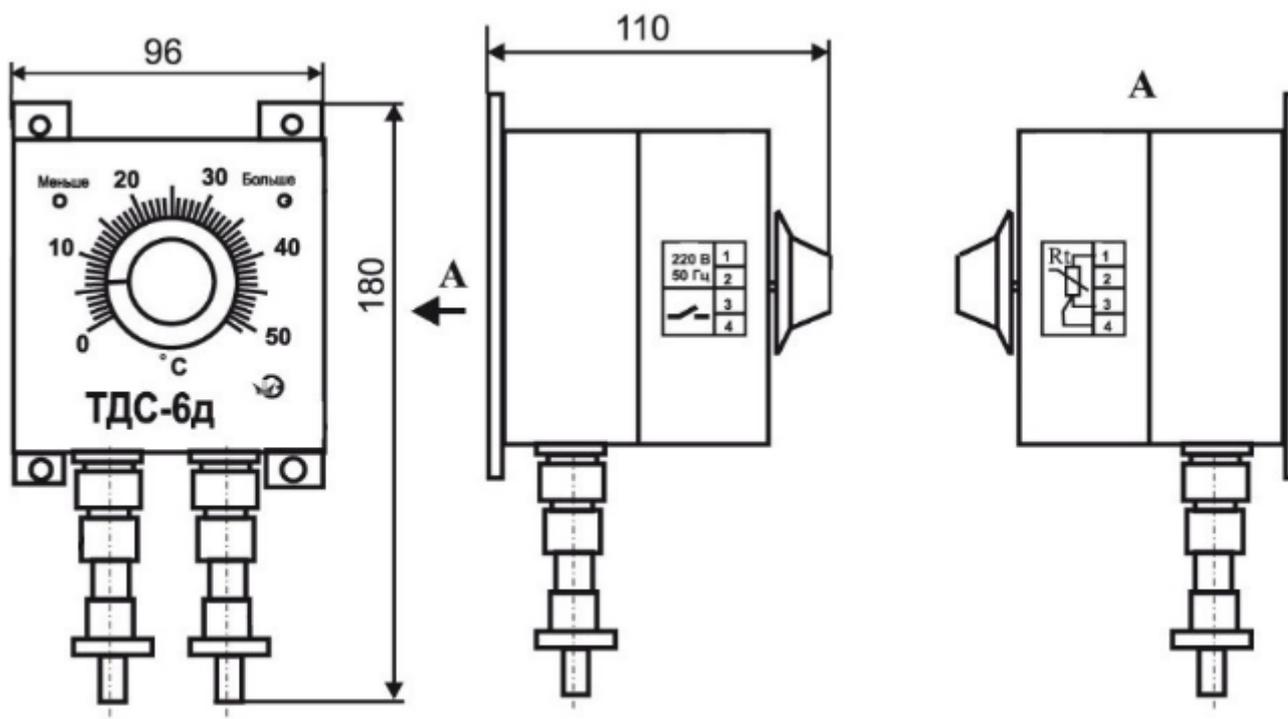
Внешний вид и габаритные размеры регулятора ТДС-д с разъемами
